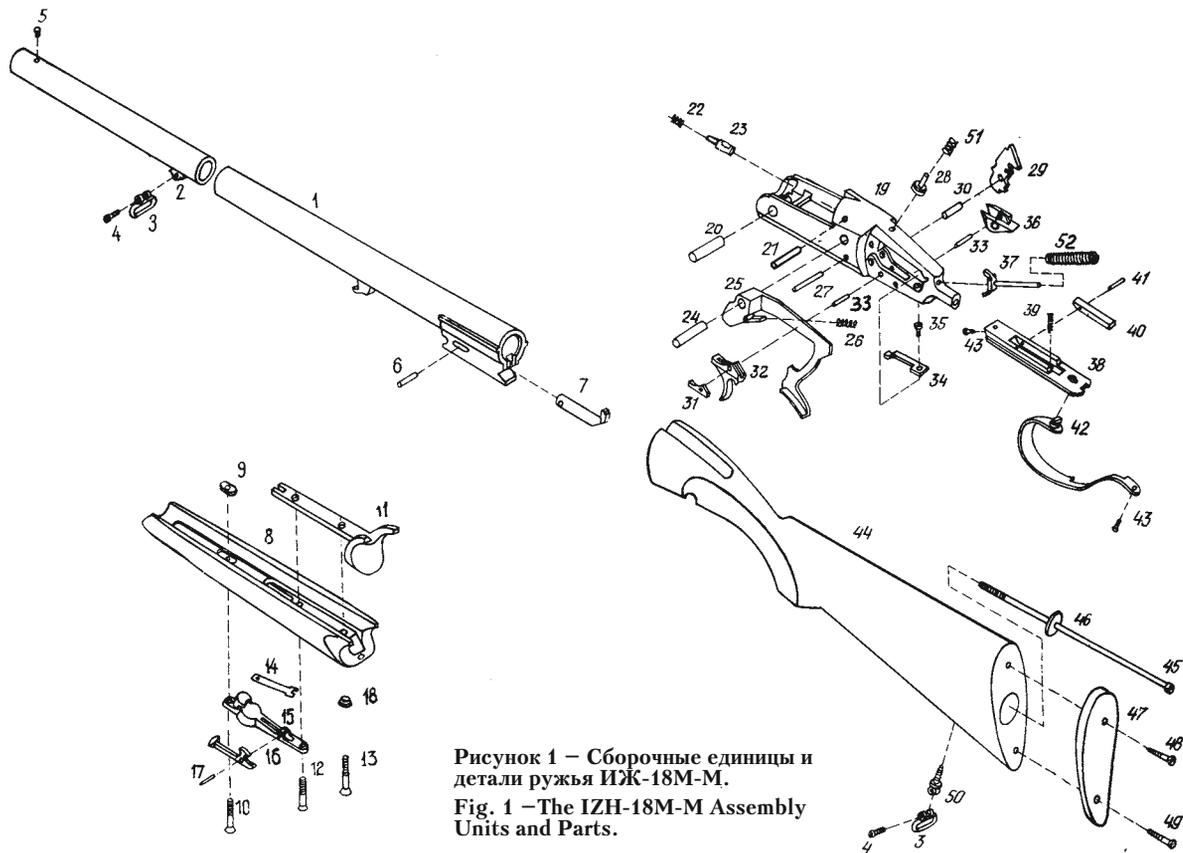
Сборочные единицы и детали ружья ИЖ-18М-М.
